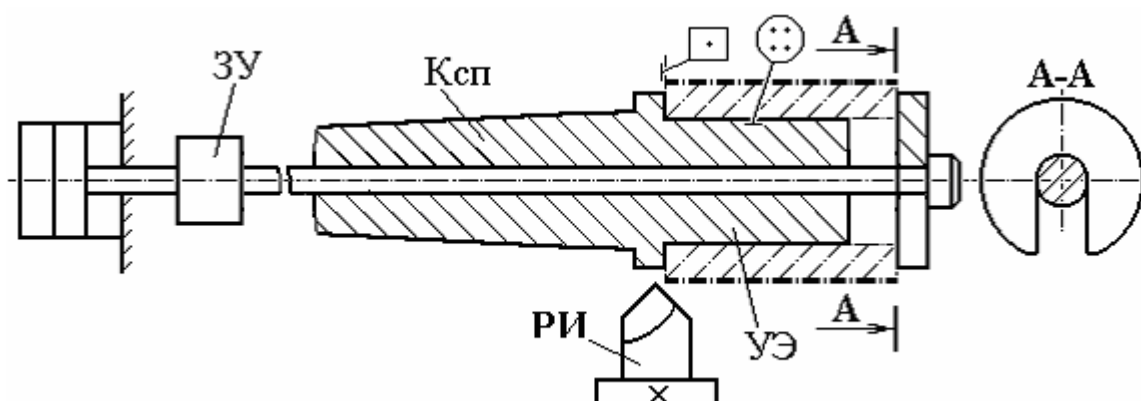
Принципиальная схема станочного приспособления (СП) типа «Оправка»
